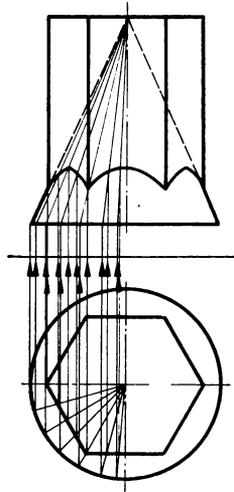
Durchdringung einer Rechthcksäule mit Kegel
